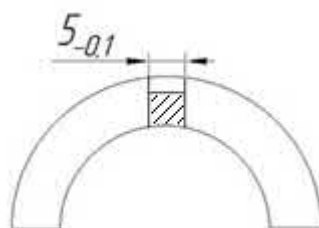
Схема отбора образцов для испытаний на растяжение от трубной заготовки Ø63,5×37,5 мм сплава Э110
